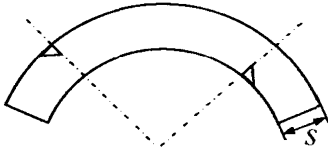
Подготовка рабочей поверхности ПЭП
